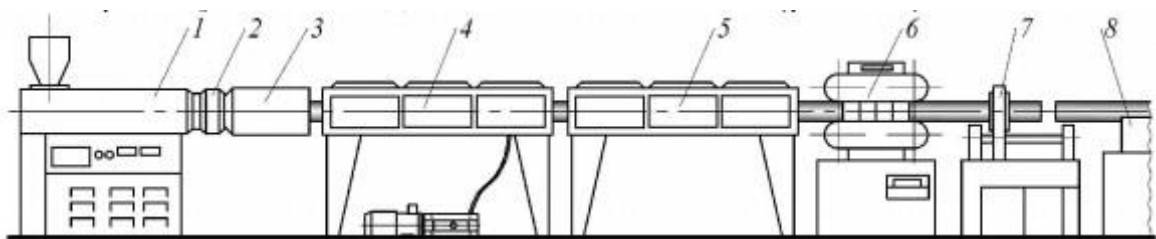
Принципова апаратно-технологічна схема виготовлення гладких полімерних труб: 1 – екструдер; 2 – трубна головка; 3 – калібрувальний пристрій; 4 – вакуум-ванна; 5 – ванна зрошення; 6 – тягнучий пристрій; 7 – відрізний пристрій; 8 – приймальний пристрій
